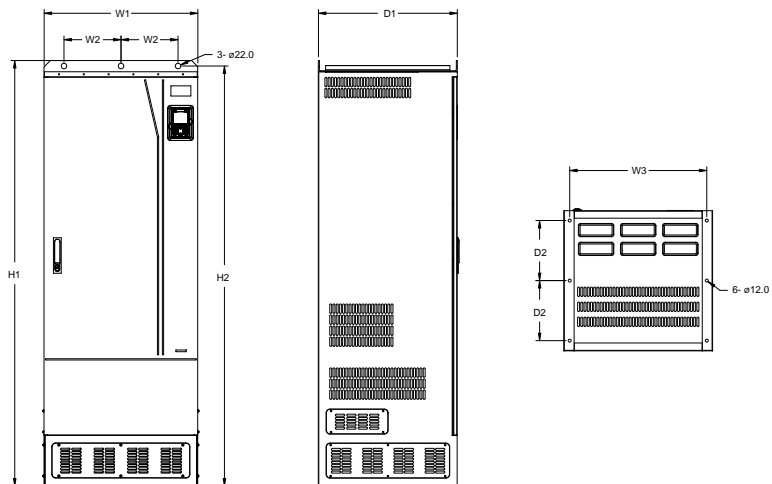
Схема для напольного монтажа ПЧ напряжением 660 В, от 400 до 630 кВт
